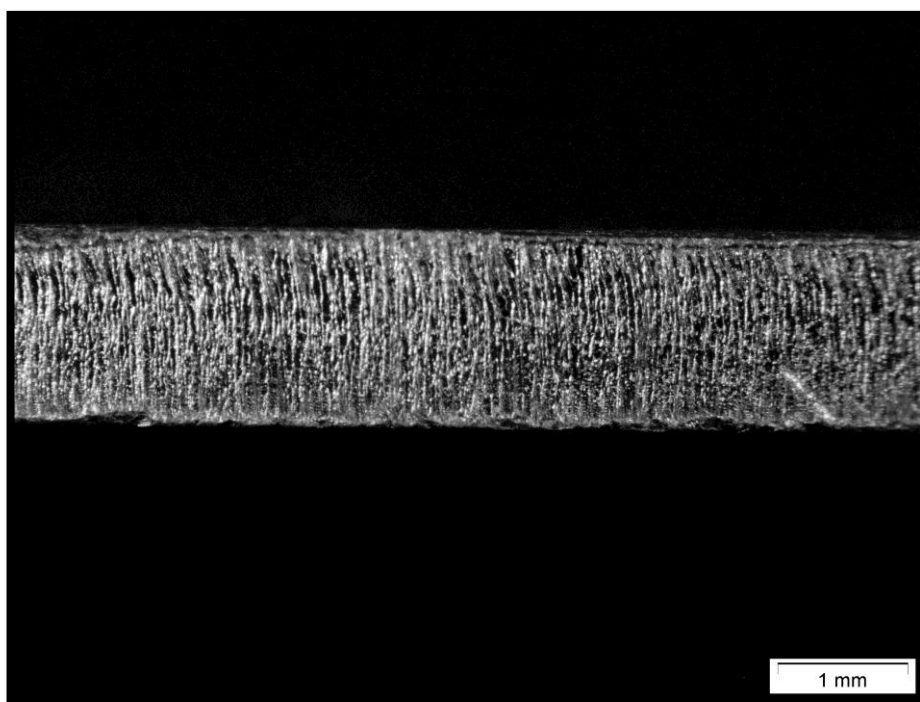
Detalhe de um corte a laser em amostra de alumínio.
